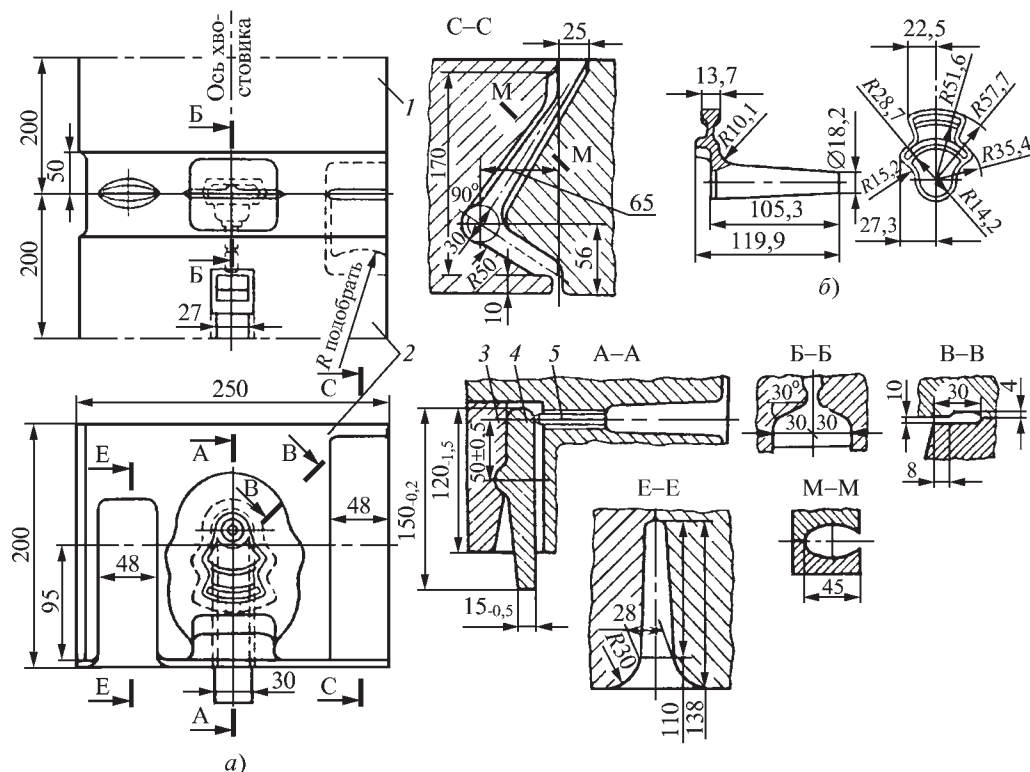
Молотовый штамп (а) и горячая поковка (б) типа стержня с несимметричным фланцем: 1 — верхний штамп; 2 — нижний штамп; 3 — пластина; 4 — рычаг; 5 — выталкиватель
